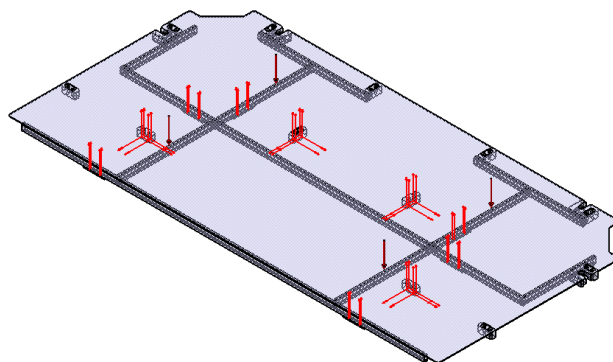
Aplicación de las C. C sobre el conjunto soldado del suelo.
